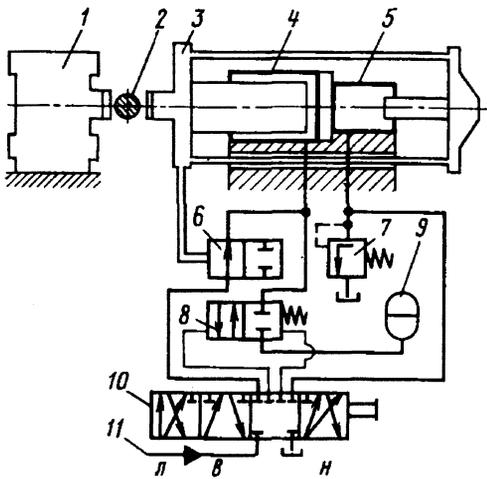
Гидравлическая схема прессы для ломки заготовок
